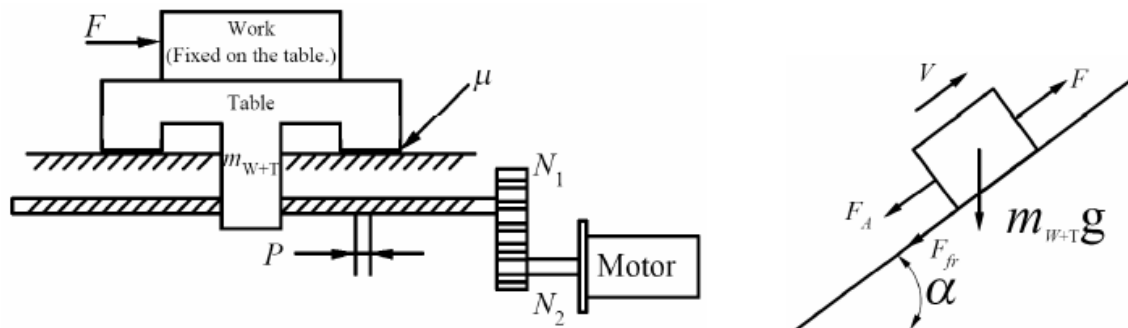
Representação da transmissão mecânica por engrenagens e fusos.
